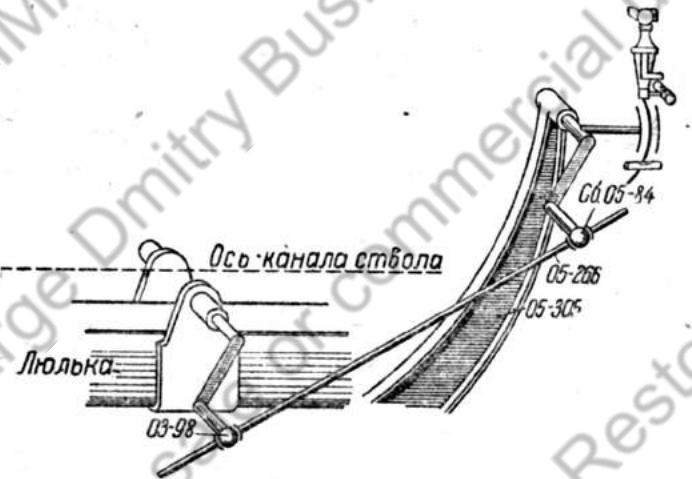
Схема соединения прицела с качающейся частью пушки:
